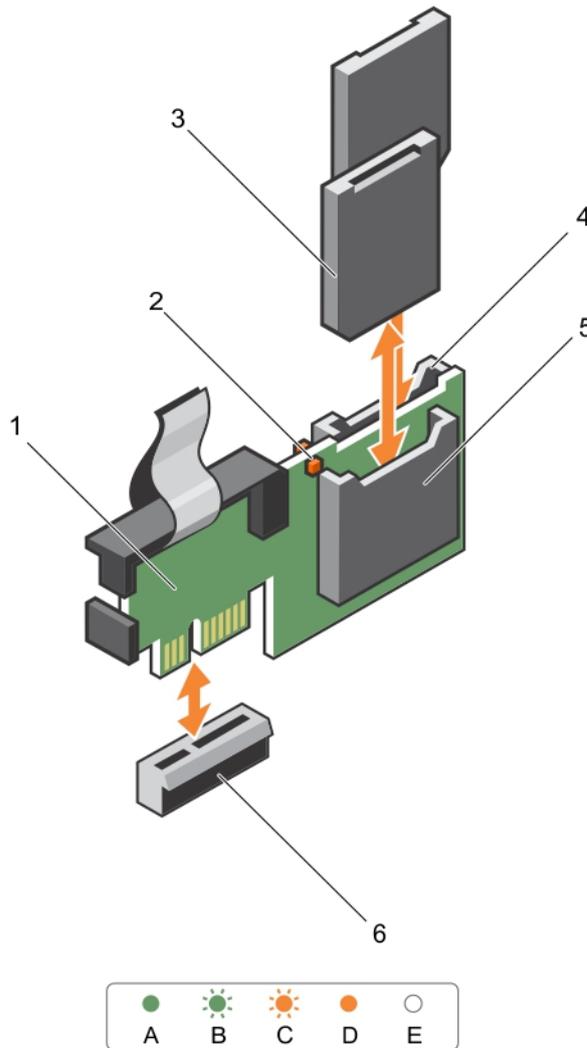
Como remover e instalar o IDSDM (Internal Dual SD Module)
